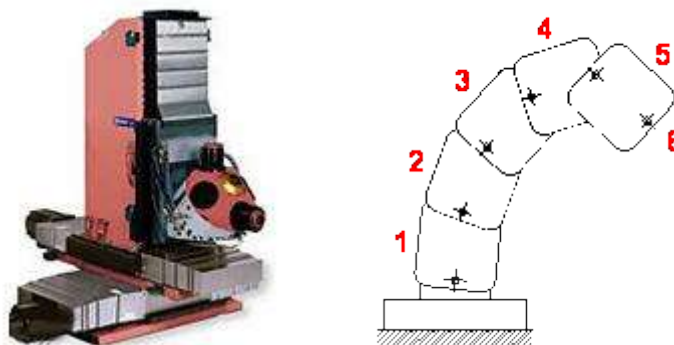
Робот с последовательной кинематикой, обслуживающий металлообрабатывающий станок
